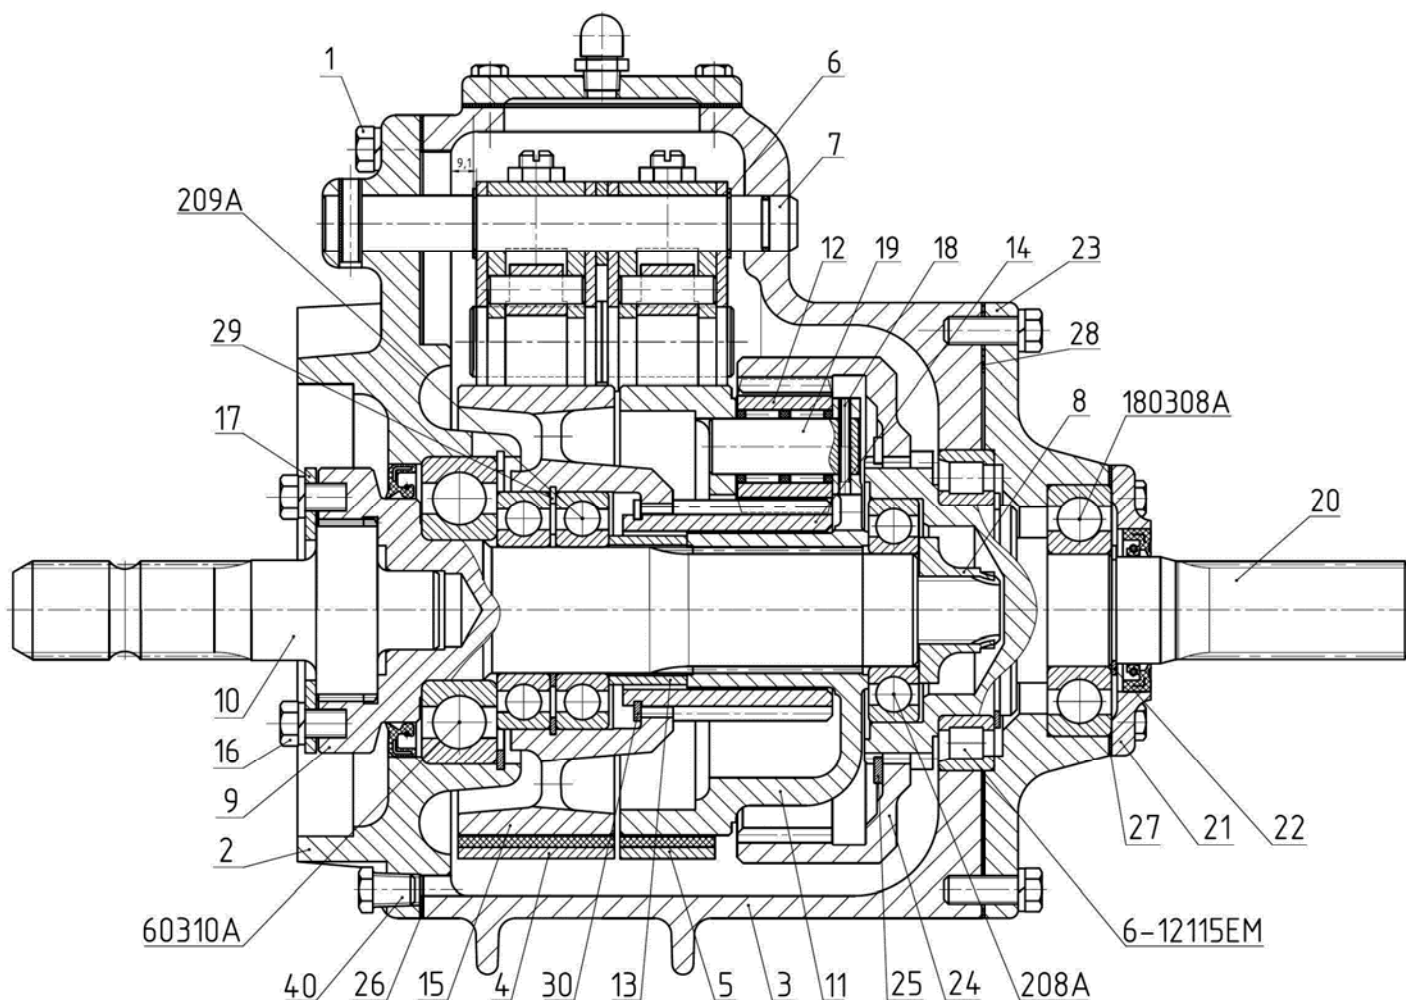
Редуктор ВОМ 2522-4209015А.
